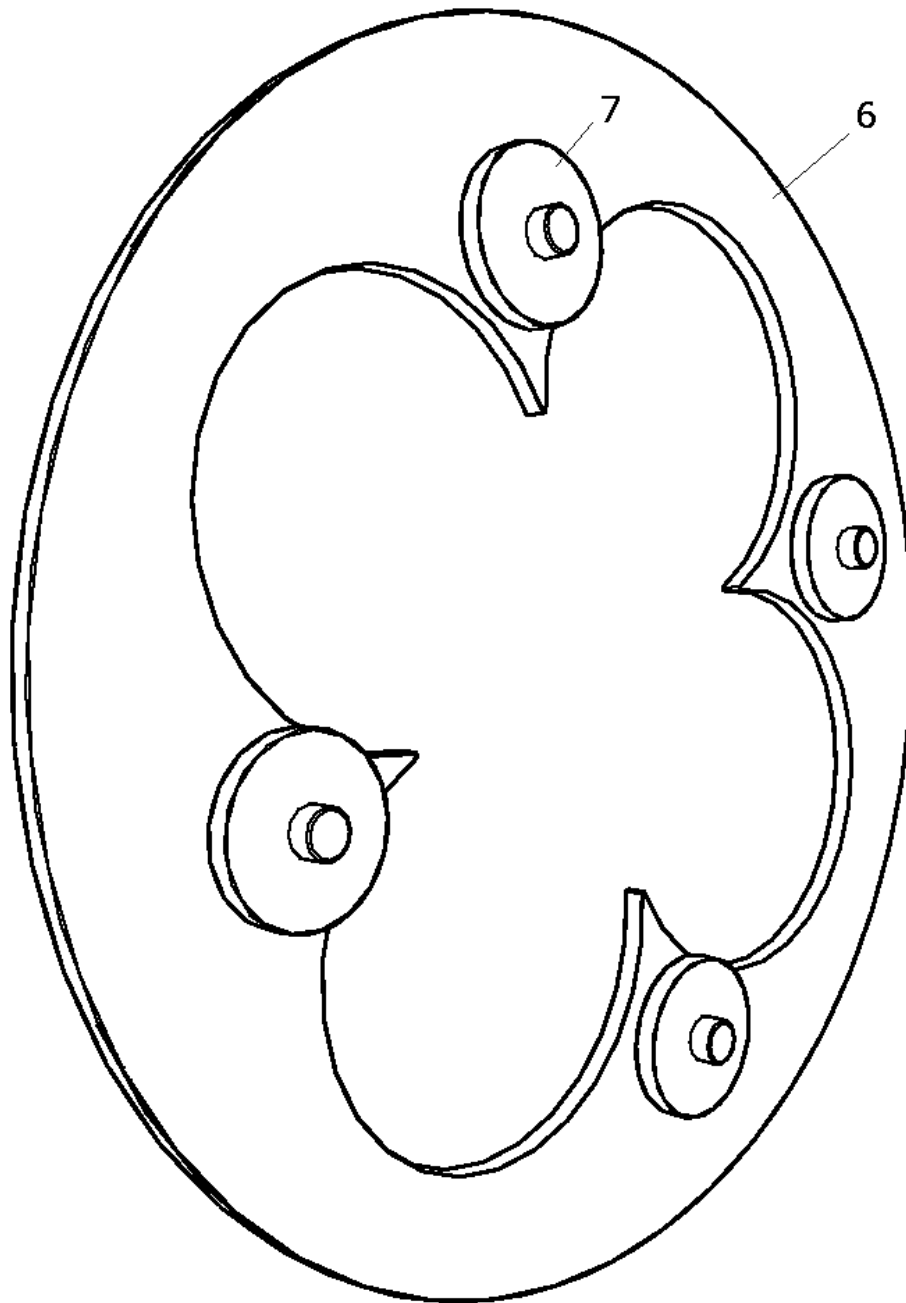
Drehkolben-Stirlingmotor, abgebaut bis hinter die erste Ofendichtung.
